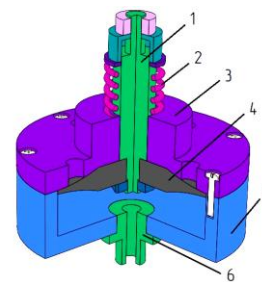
Схема зворотного клапана мембранного типу: 1 – шток; 2 – пружина; 3 – кришка; 4 – гумовий пелюстковий клапан; 5 – корпус; 6 – штуцер
